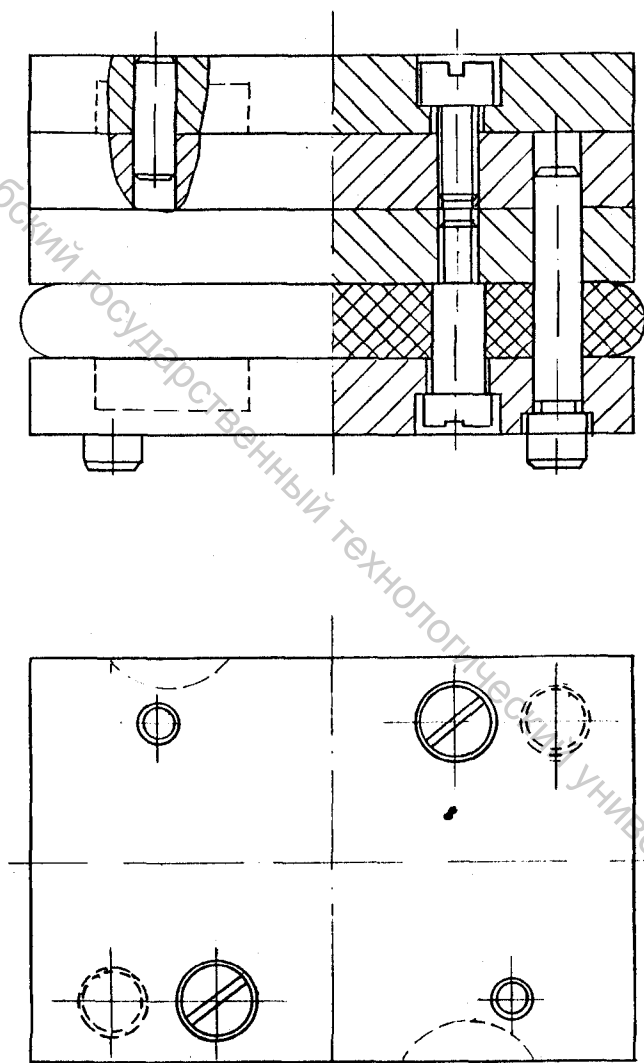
Сменный пакет с верхним расположением матрицы.
